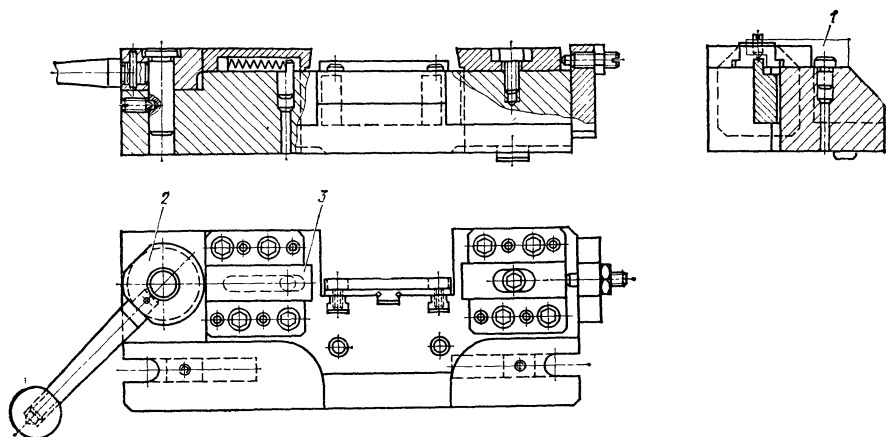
Эксцентриковое наладочное приспособление для фрезерования валиков (наладка 1 крепится эксцентриком 2 через планку 3 с боковым скосом)
